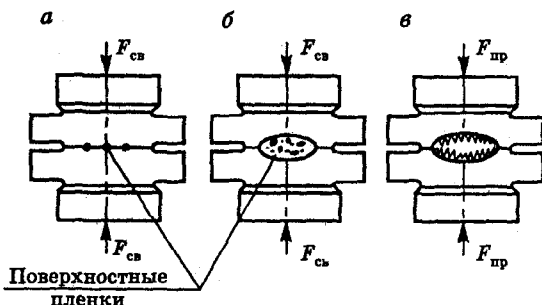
Этапы образования соединения при точечной сварке: а — сжатие; б — сварка; в — проковка
